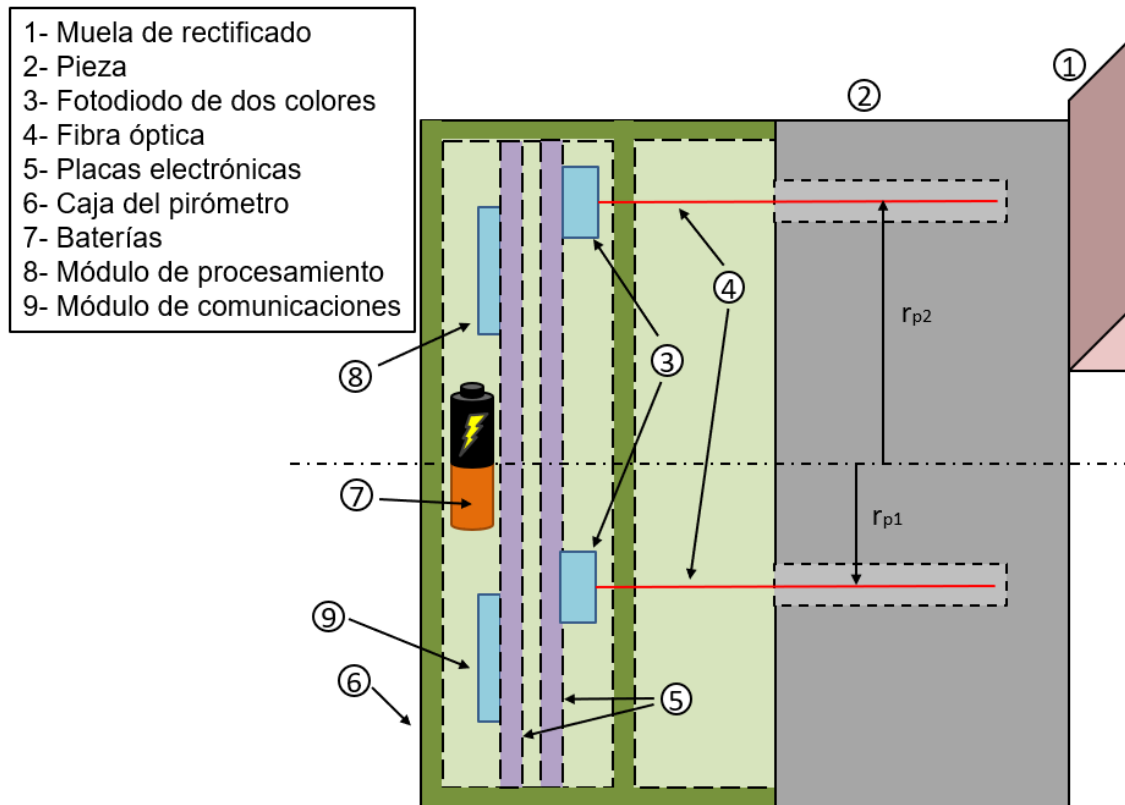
Disposición de los principales componentes del montaje del pirómetro rotativo
